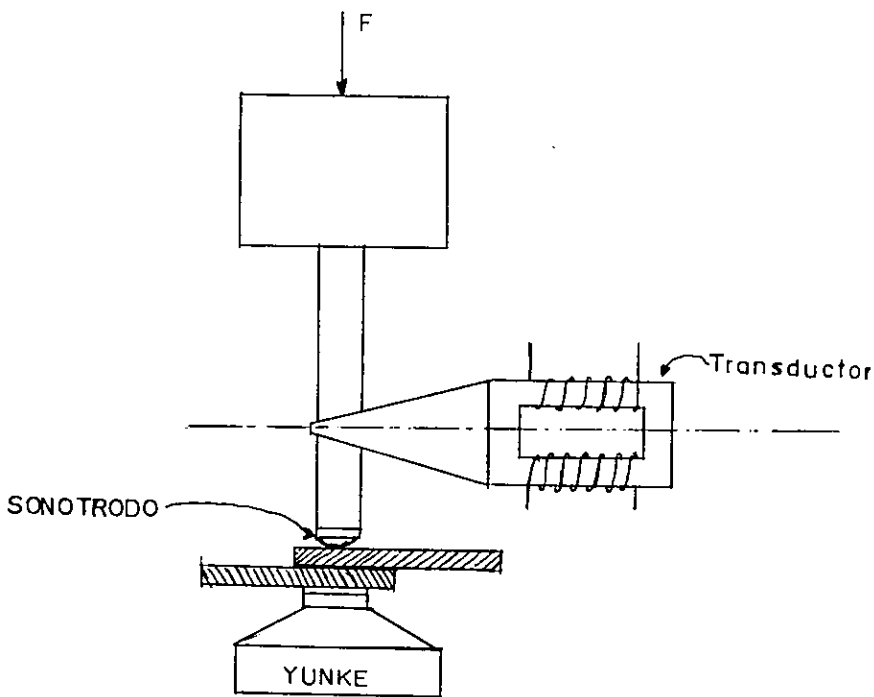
SOLDADURA POR ULTRASONIDO
